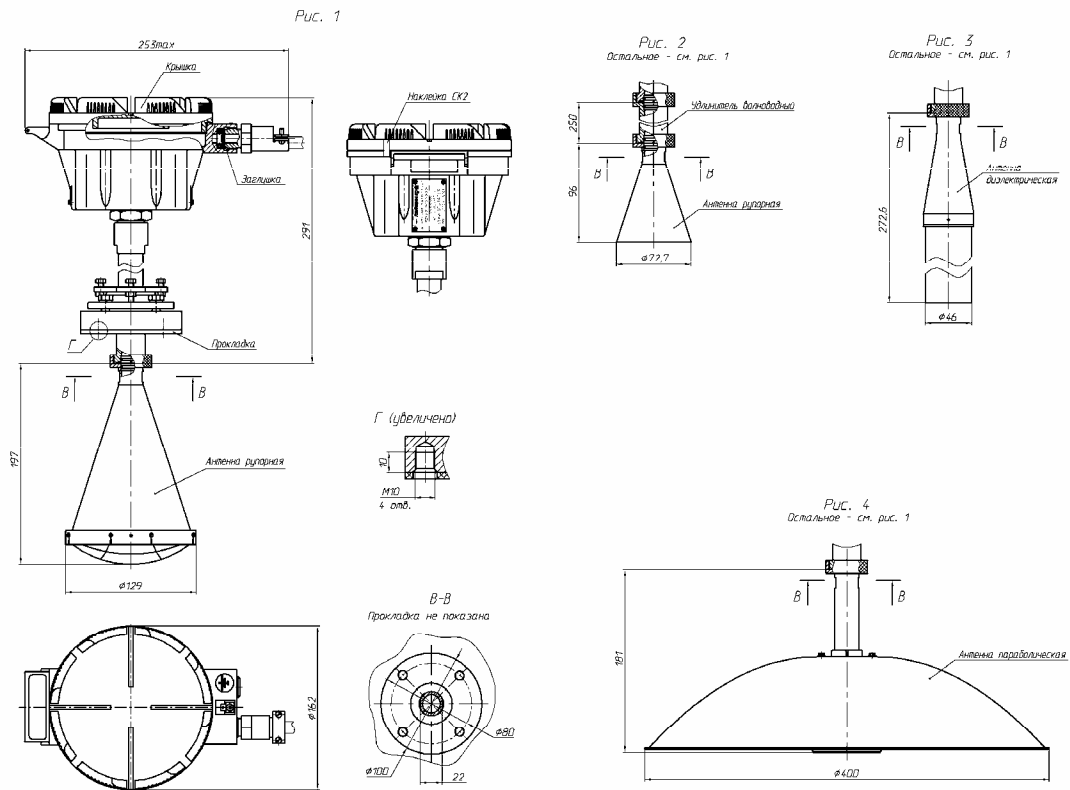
Габаритные и установочные размеры датчиков РДУЗ-00, РДУЗ-01, РДУЗ-10, РДУЗ-20, часть 1
